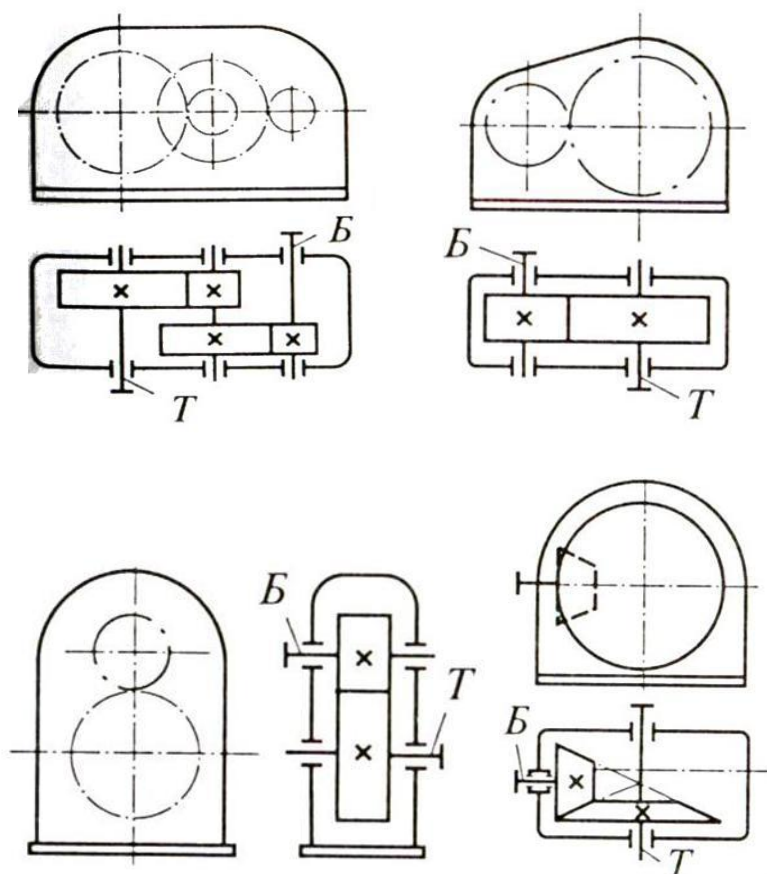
Кинематические схемы цилиндрических редукторов.
